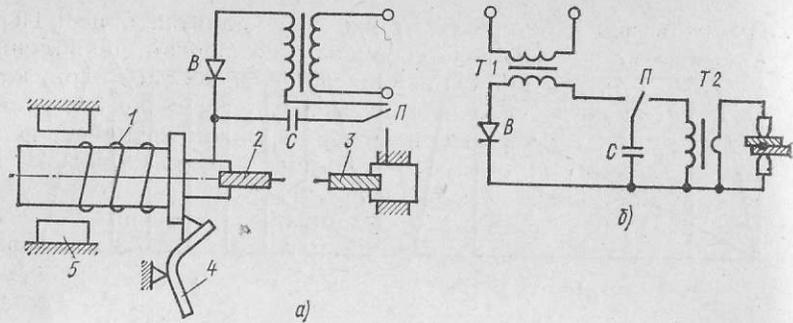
Схемы конденсаторной сварки:
